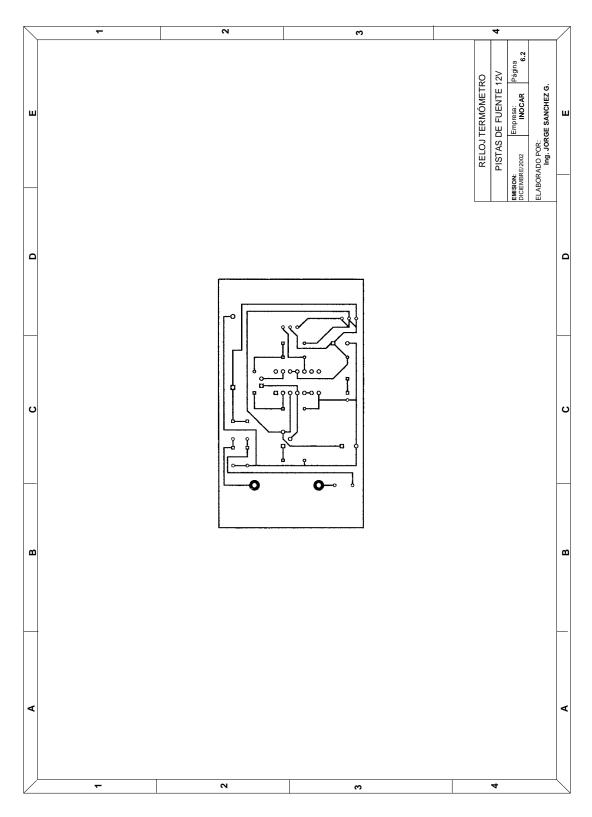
Tarjeta de fuente 12VDC(Diagrama de pistas lado de soldadura)
